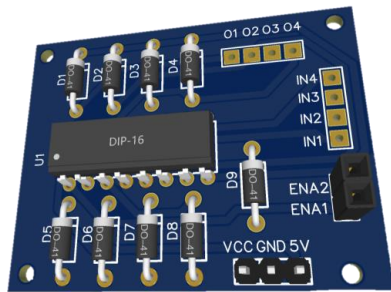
Diseño capa inferior PCB módulo driver puente H.
